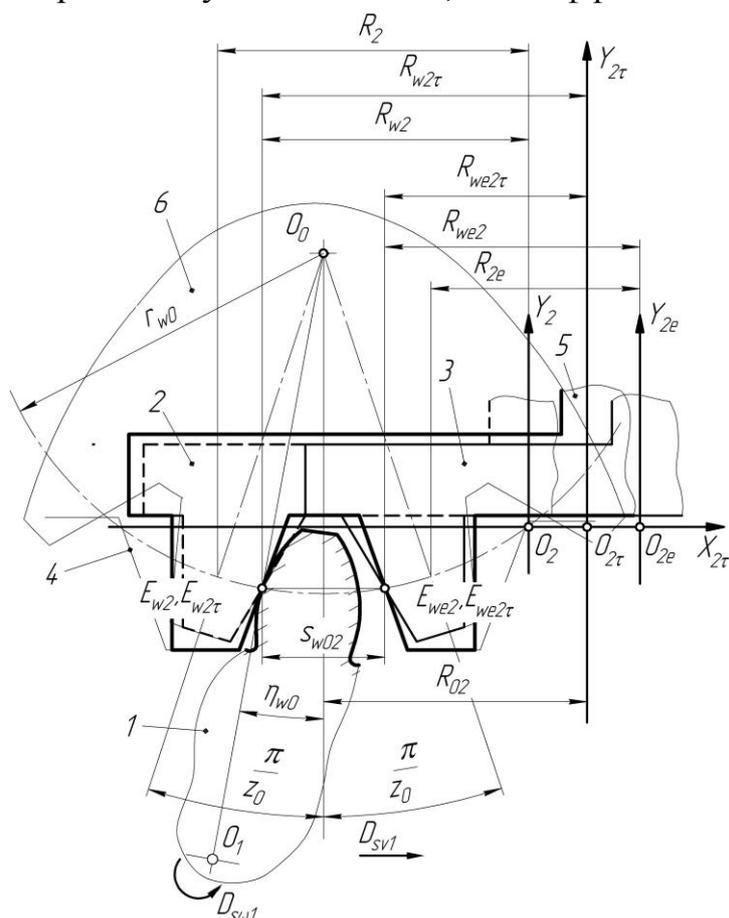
Схема к расчёту радиусов чистовых резцовых головок для обработки зубьев шестерни
